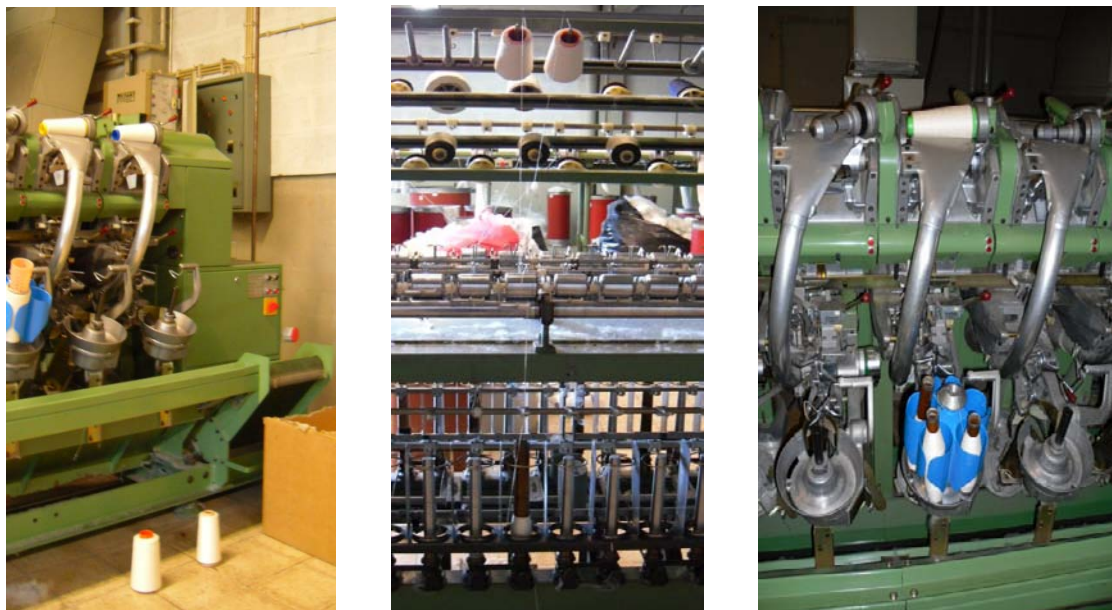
Bobinagem do fio a 1 cabo, Retorção e Bobinagem do fio a 2 cabos
